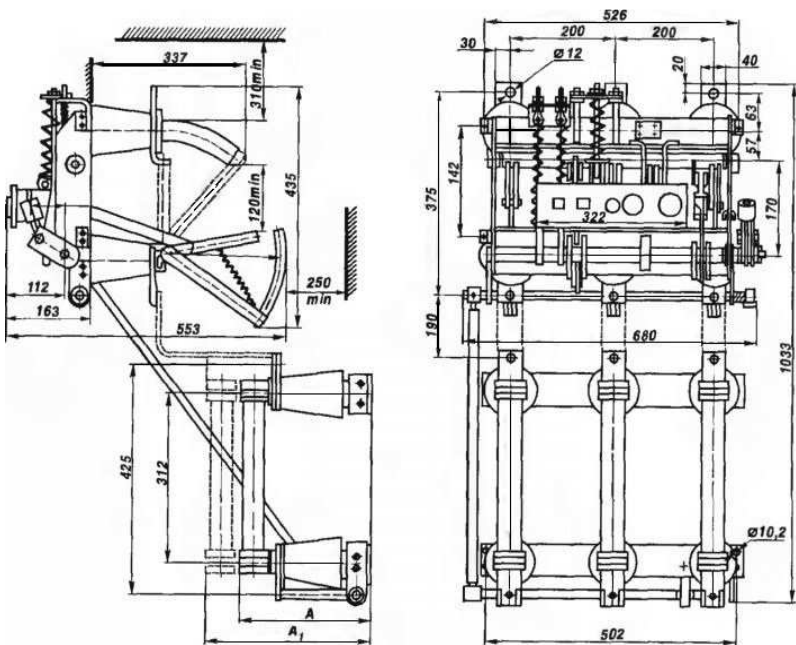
Выключатель нагрузки типа ВНП-10/630-20
